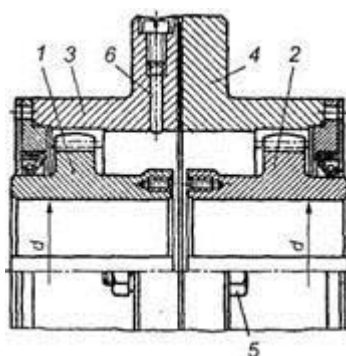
Зубчатая муфта: 1, 2 - полу муфты с наружными зубьями;
